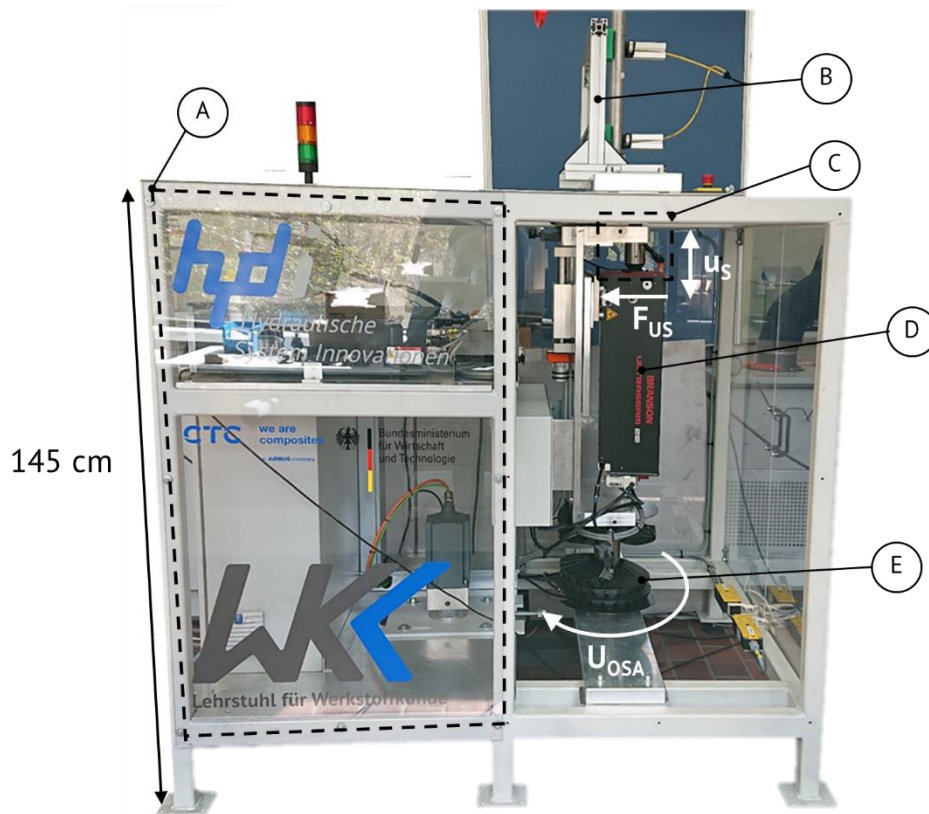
Übersichtsdarstellung der Orbitalschweißanlage A) Mess- und Regelsysteme, B) Einspannvorrichtung, C) Schweißbereich, D) Schweißaktuator und E) Drehachse
